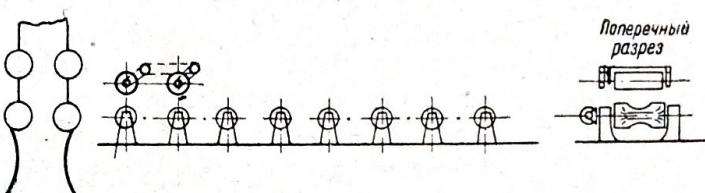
Прямой конвейер с креплением бревна верхними рифлеными валиками
